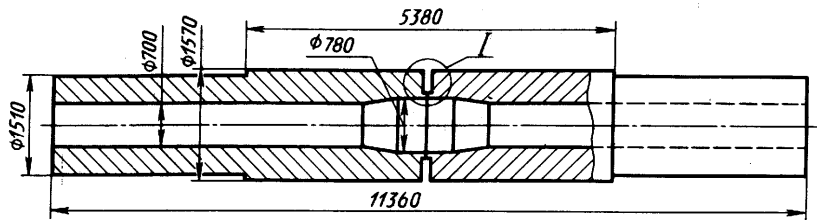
Вал в процессе электрошлаковой сварки
